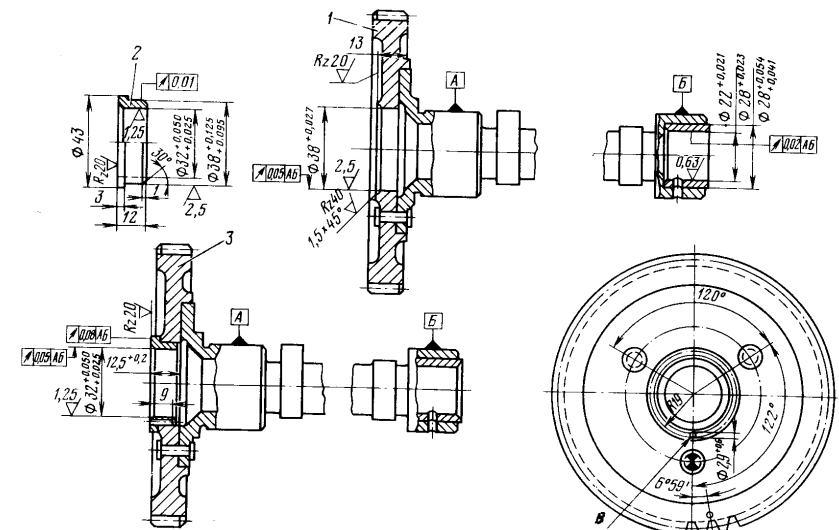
Расточка шестерни распределительного вала под ремонтную втулку:
